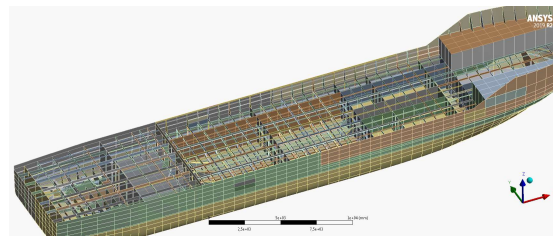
Cubierta de doble fondo. Fuente: elaboración propia
